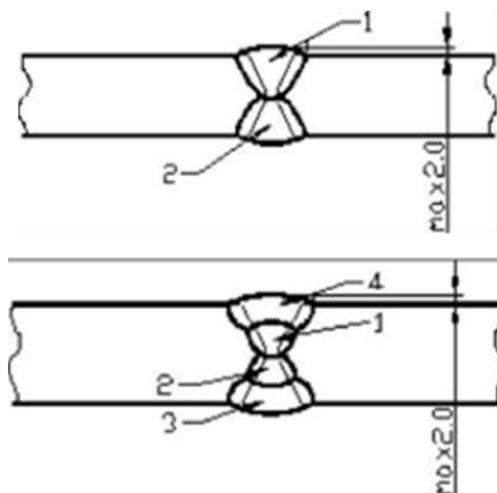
Схема выполнения вертикального сварного шва стенки 5 мм
